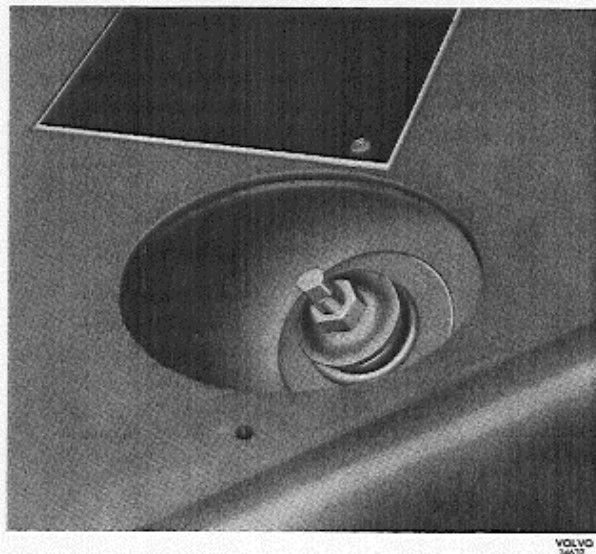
Obere Befestigung des hinteren Stoßdämpfers, P 1800
